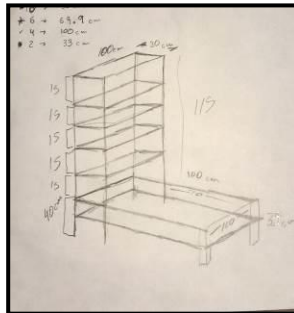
Planos a mano alzada del deshidratador a escala 1:2.
